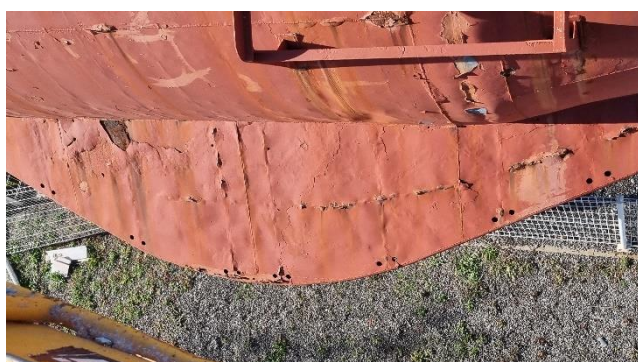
Vue générale du stabilisateur bâbord, avec forte corrosion des zones de soudure et d'une partie en assemblage avec la coque
